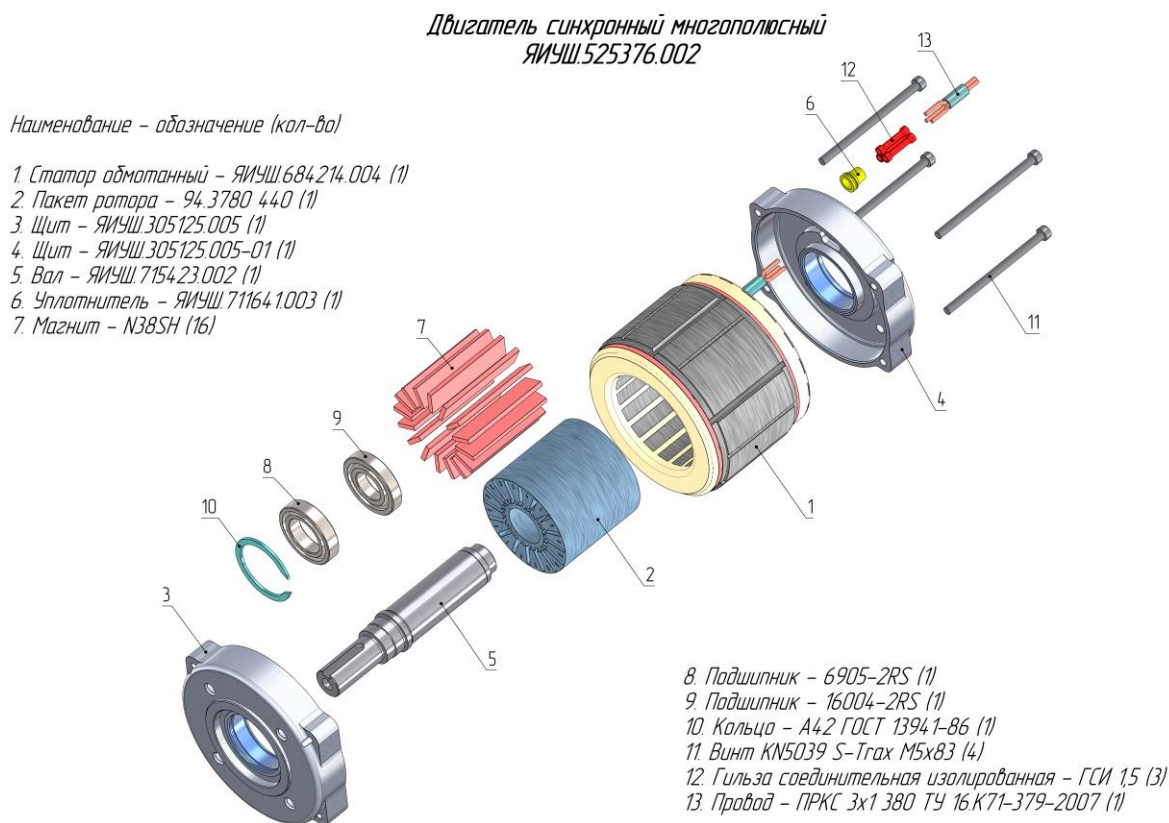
синхронный многополюсный двигатель ЯИУШ.525376.002
